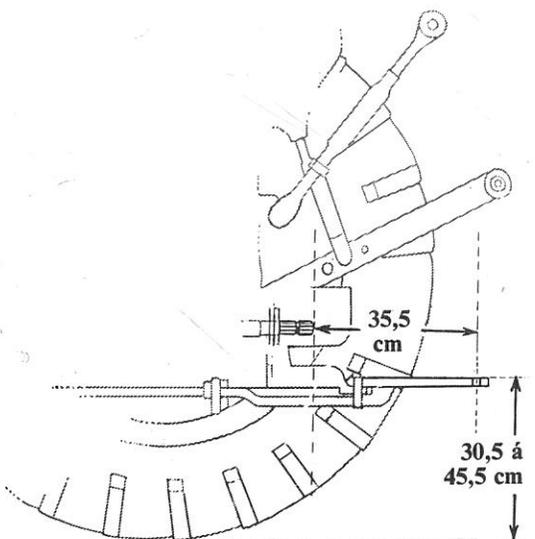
Dimensions normales de la barre d'attelage et de la prise de force considérées dans les instructions pour l'attelage.
